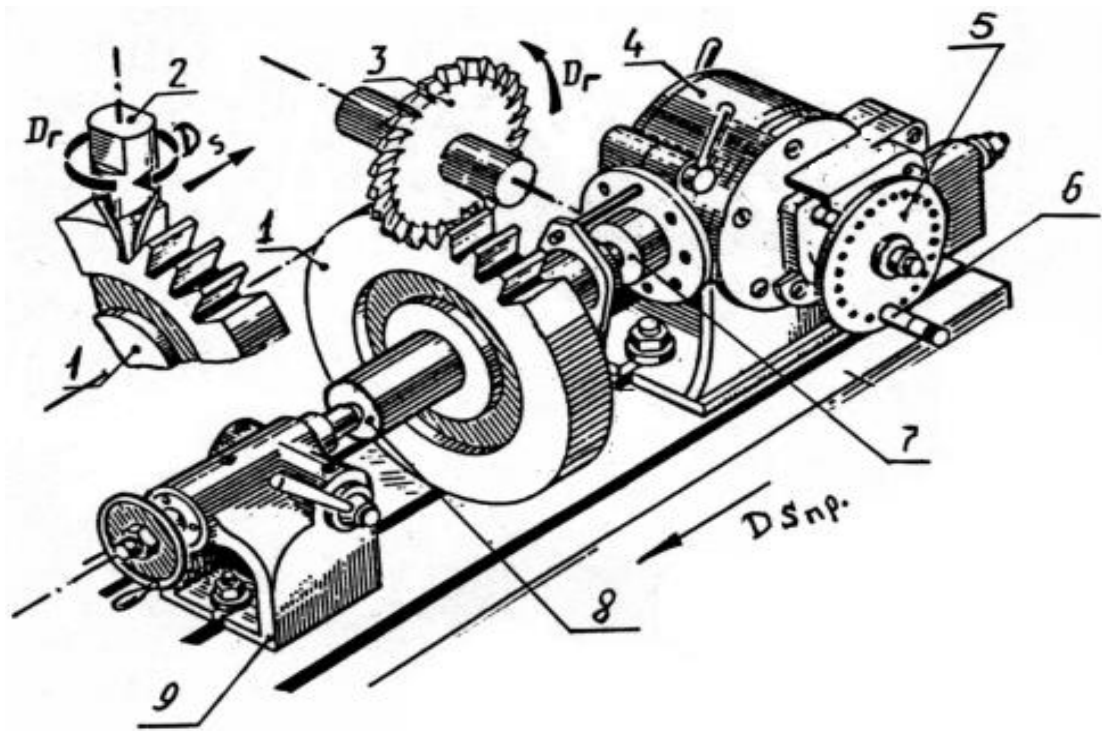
Схема фрезерования в делительной головке:
